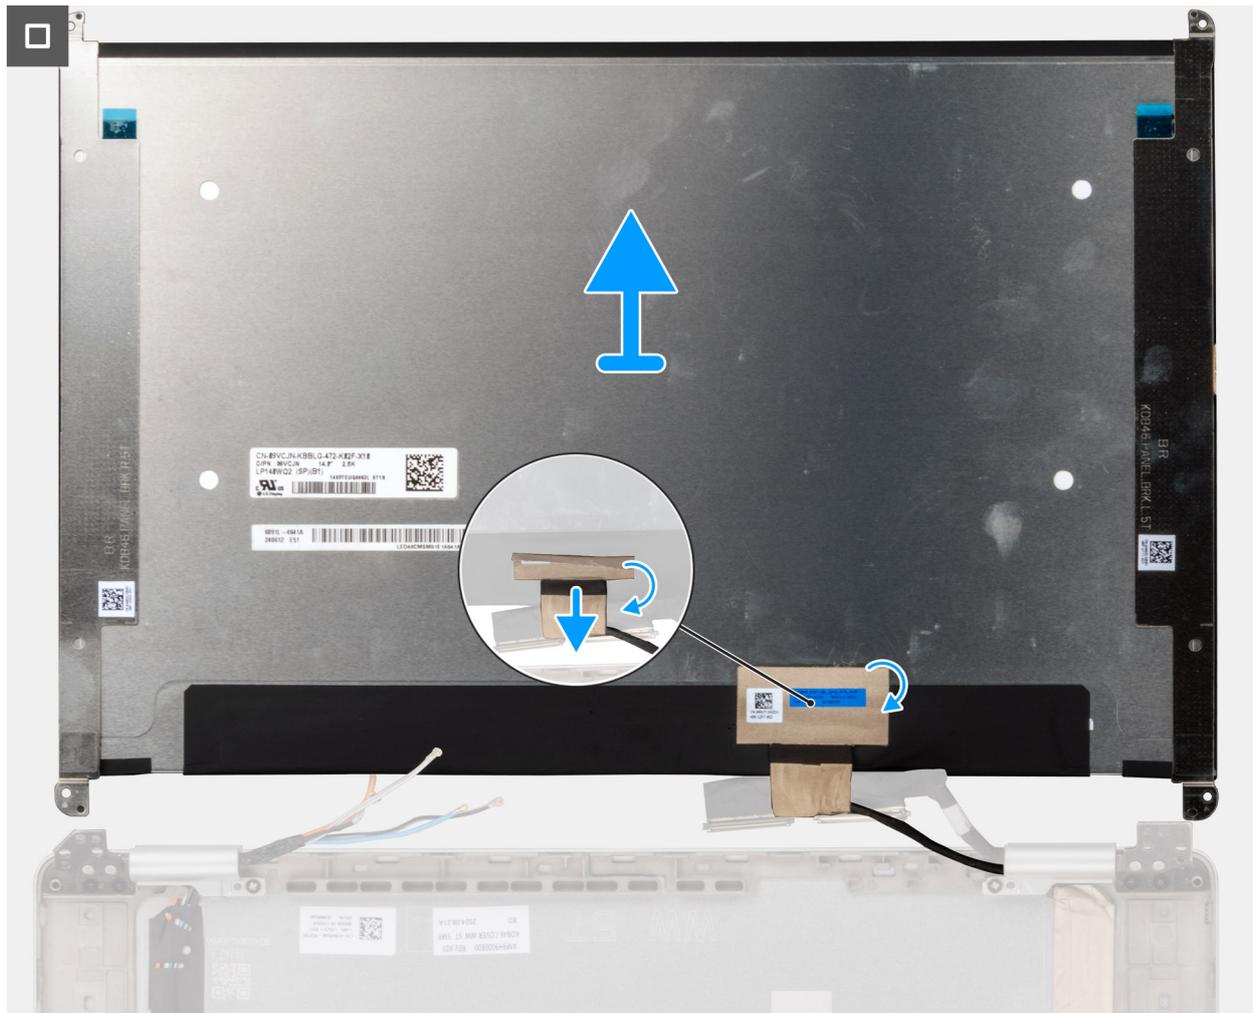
Extracción del cable de pantalla de la cubierta posterior
